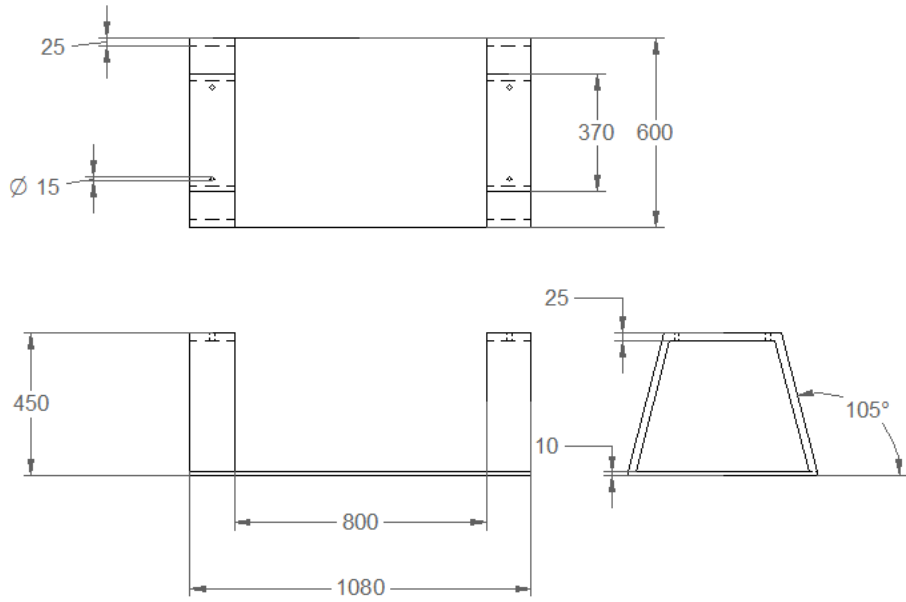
Plano estructura soporte del horno. Fuente: Autor
